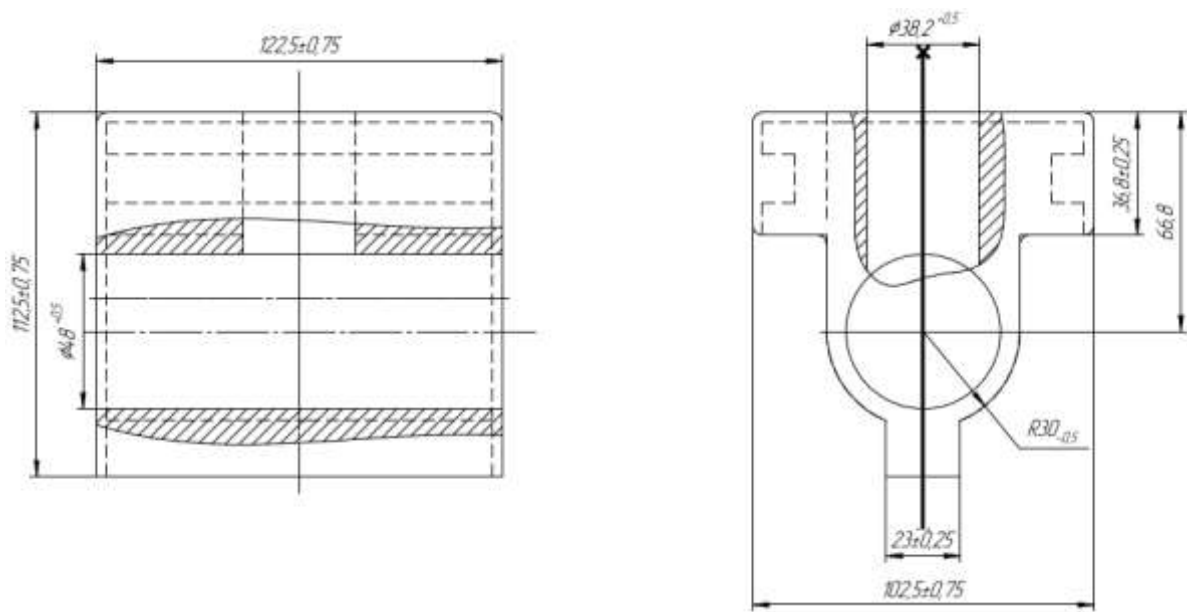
Ескіз заготовки з піщано-глинисті форми
